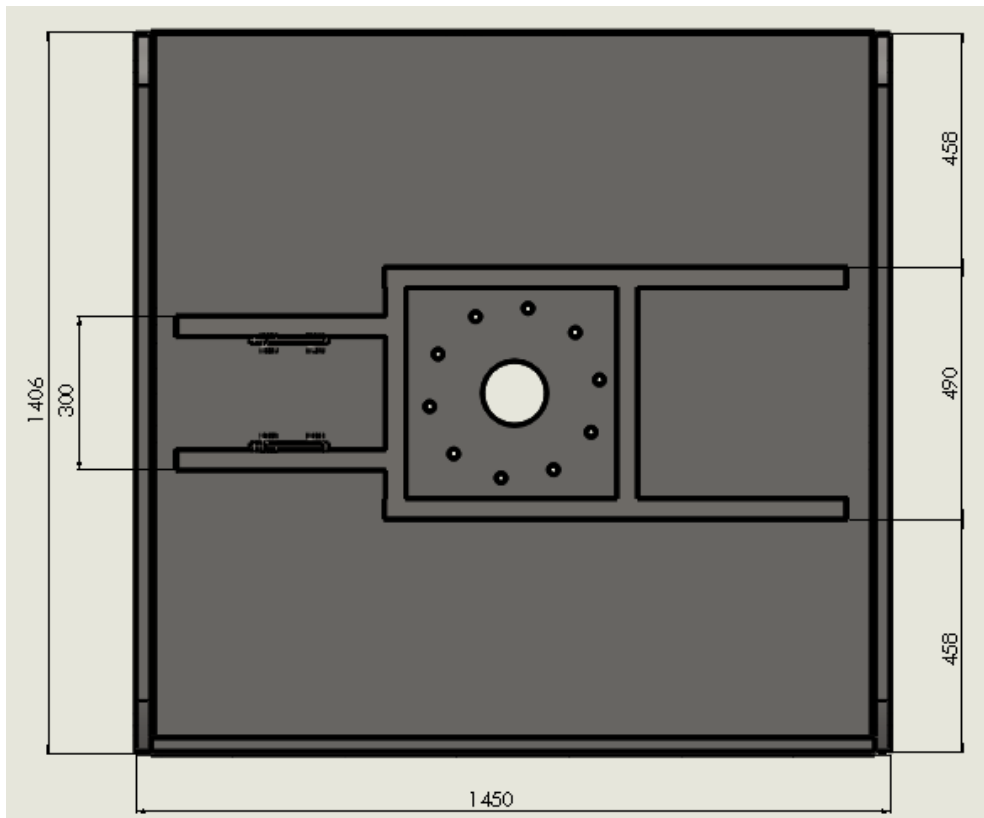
Vista superior del chasis soporte del rotor de corte.
